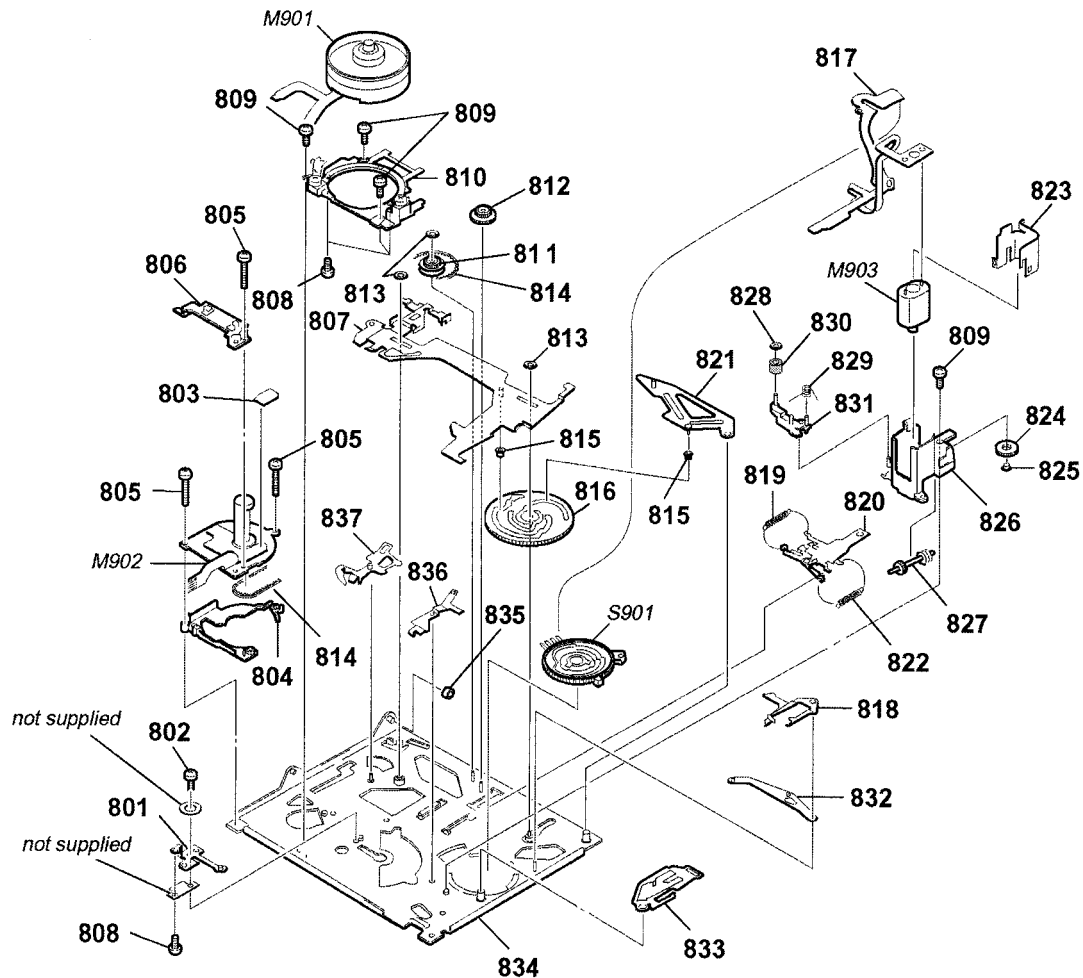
Узлы направляющих стоек, прижимного ролика, ленточного тормоза, переключатель формата, контактор блокиратора записи
